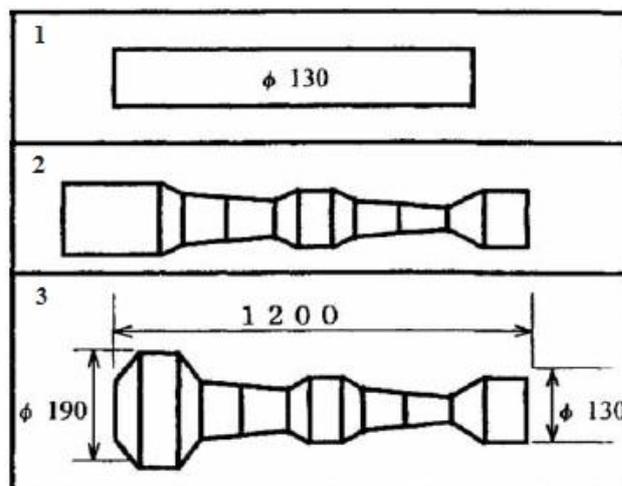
Технологическая схема получения полуфабрикатов: 1 – обточенная прутковая заготовка; 2 – предварительно откованная на машине GFM заготовка; 3 – заготовка после высадки
